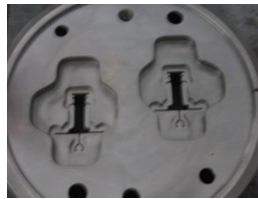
Placa hueca vista la cara de entrada del aluminio.
